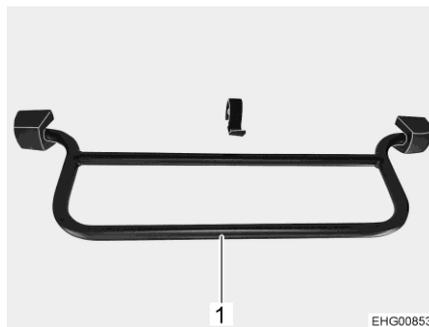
Staffa, tetto a soffietto posteriore (C 530)
